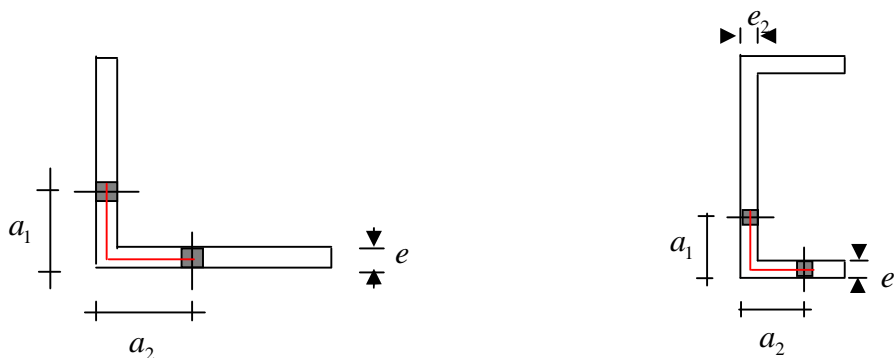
Cornières et poutre en U avec trous dans les deux ailes
